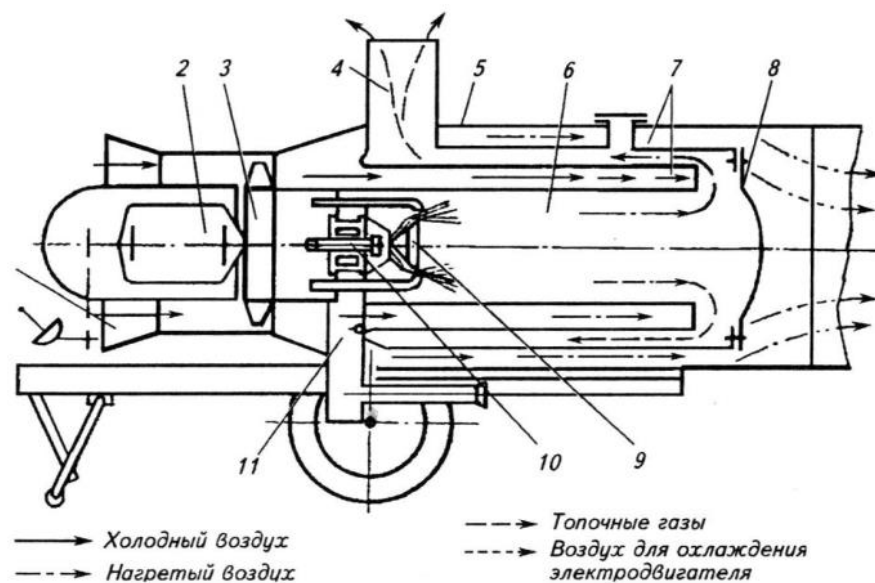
Схема рабочего процесса воздухонагревателя ВПТ-600А:
